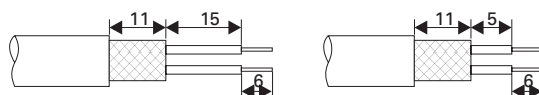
Verdrahtungsbeispiel mit Schraubadapter
